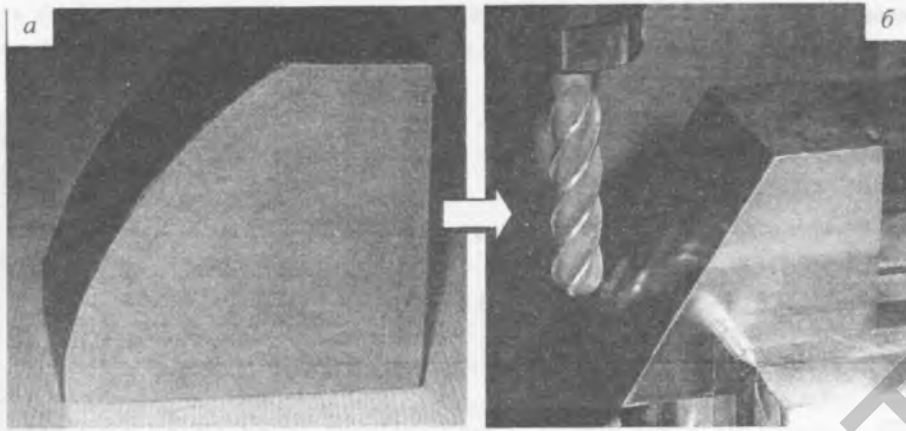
Черновая (а) и подготовленная к фрезерованию (б) заготовки
